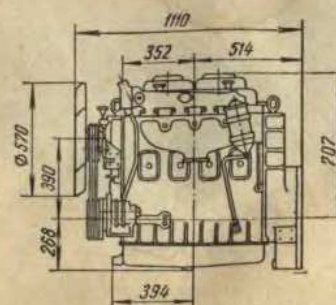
Габаритные размеры двигателя ЯАЗ-М204Г
